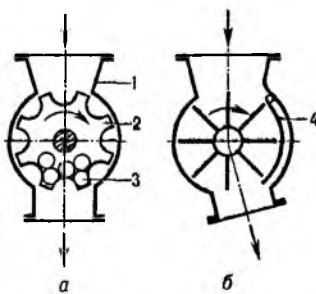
Барабанный питатель: а – ячейковый; б – секторный; 1 – корпус; 2 – барабан; 3 – шары; 4 – скребки для удаления излишка материала.
